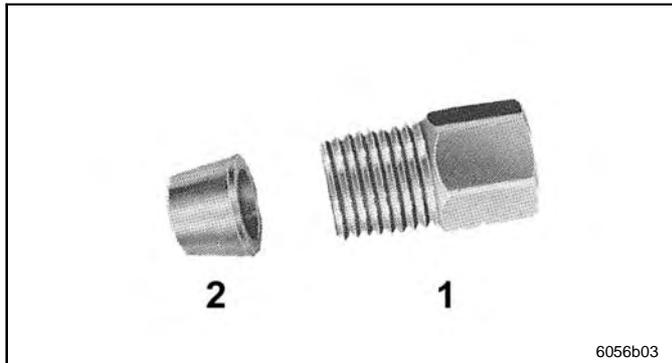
Auslassverschraubungen, schraubbar, ohne Rückschlagventil
